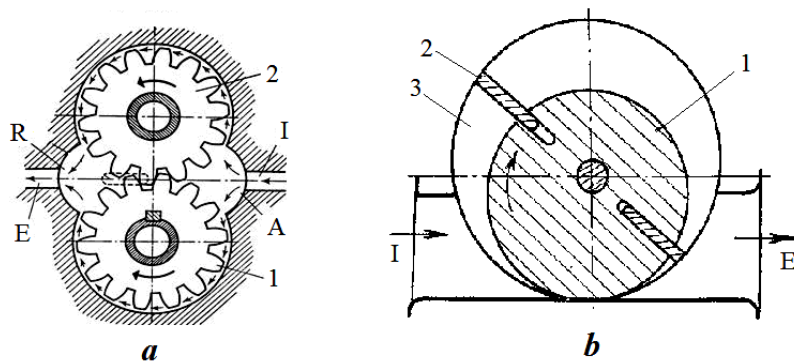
Pompe de ulei: a- cu roți dințate și angrenare exterioară: 1- pinion motor; 2- pinion antrenat; I- intrare ulei; E- ieșire ulei; A- cameră aspirație; R- cameră refulare; b- cu paletă: 1- rotor; 2- paletă culisante; 3- cameră de lucru.
